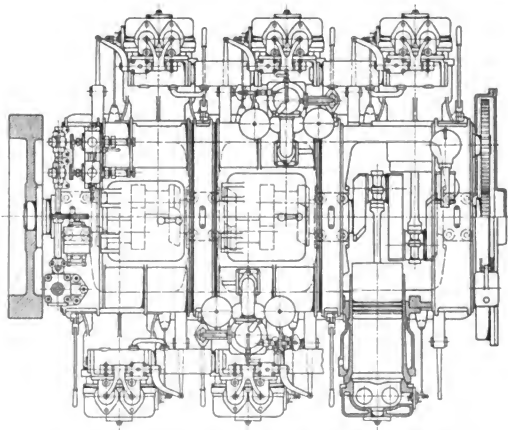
Petrolmaschine der Wolseley Tool und Motor Car Works.
